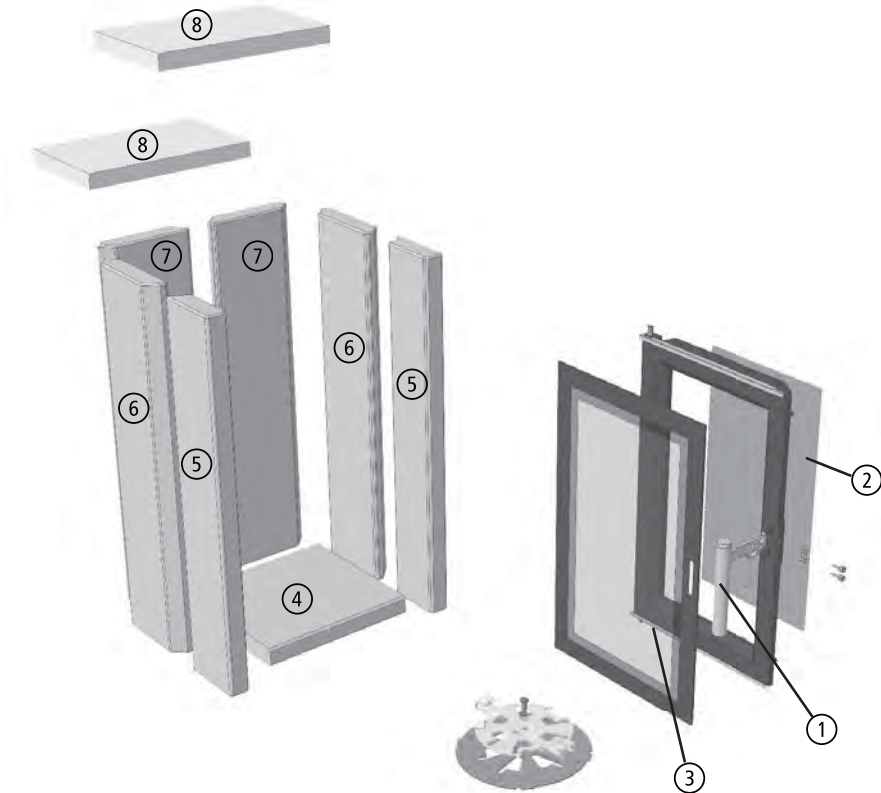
Aperçu des pièces de rechange du CORNA
